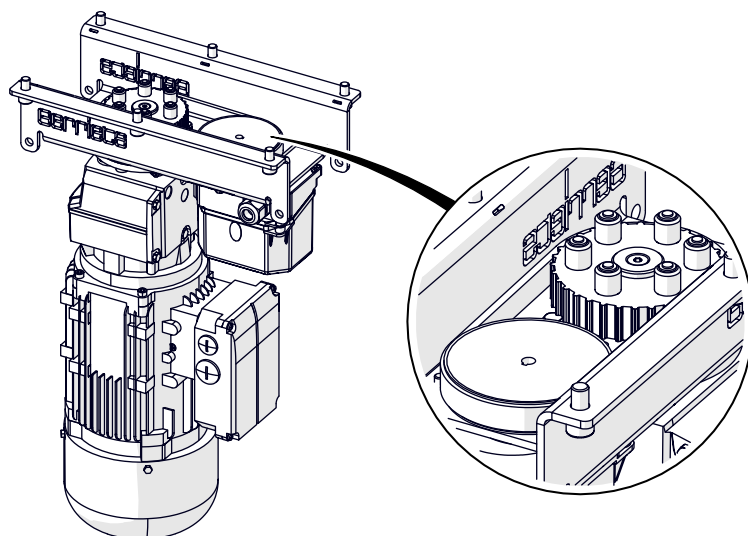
Getriebemotor – BELT DRIVE BT-L
